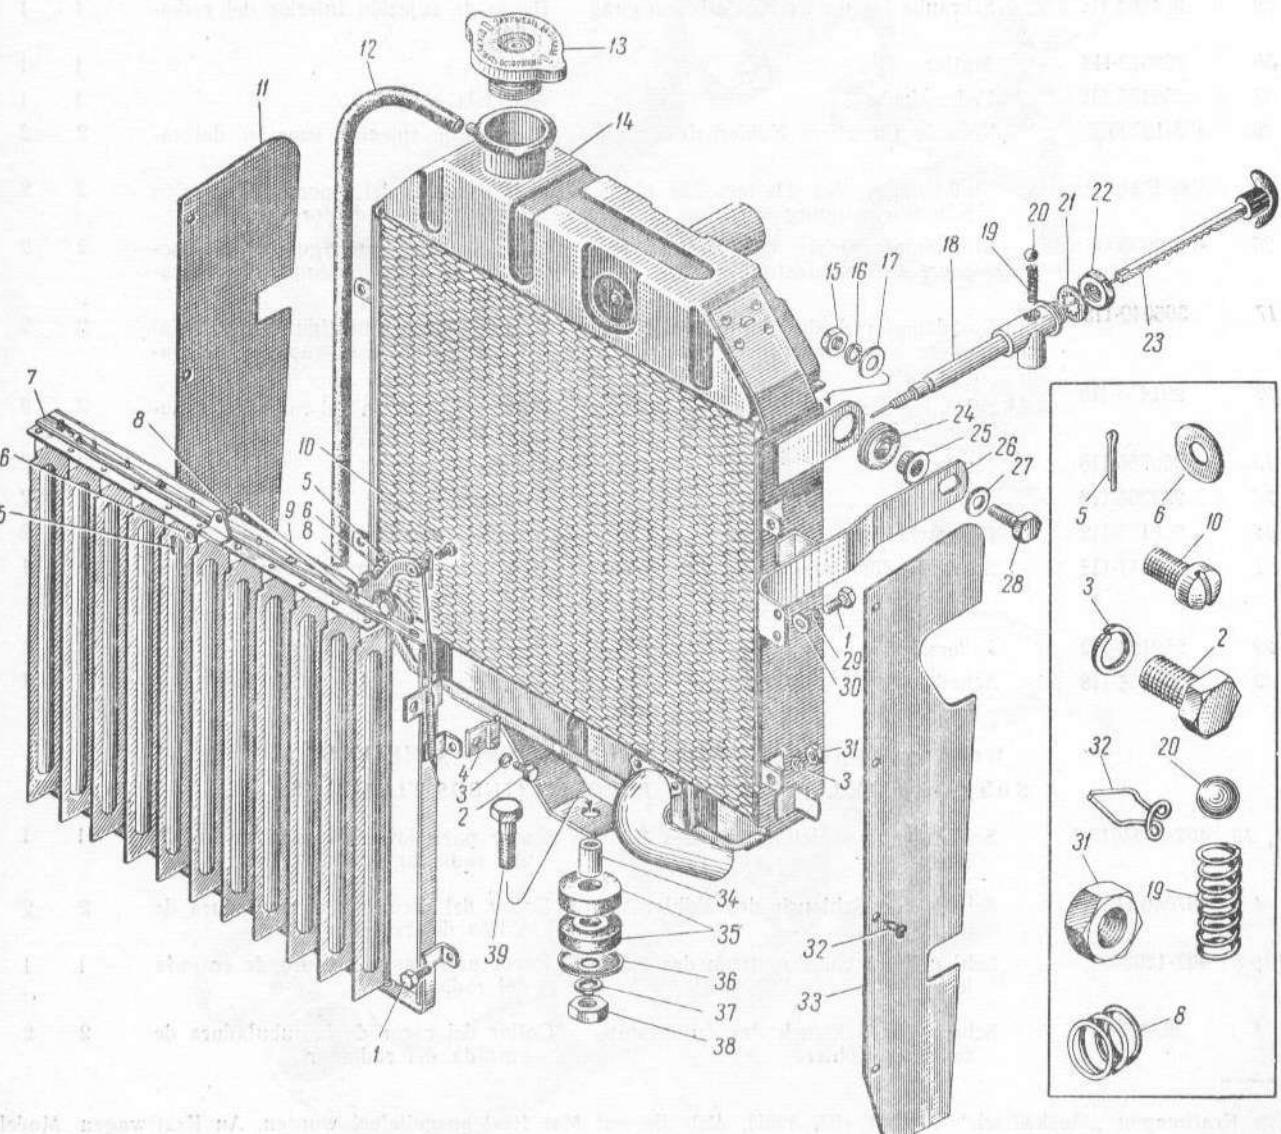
Kühler (mit Verschluß), Teile zur Befestigung des Kühlers an Rahmen und Karosserie sowie Kühlerklappenreihe
